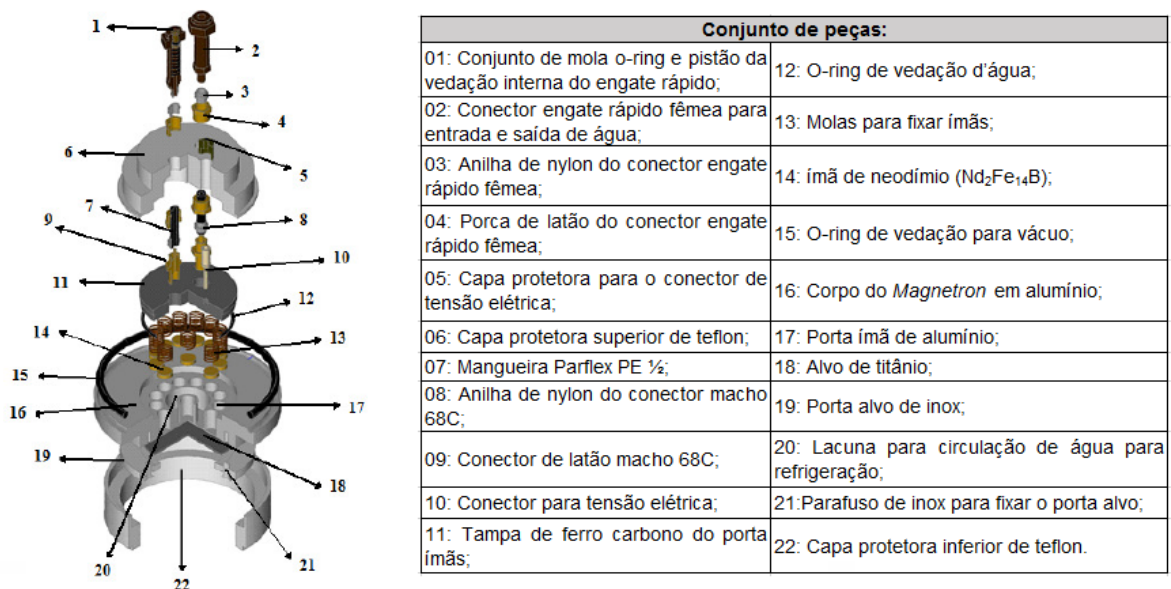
Desenho 3D do Magnetron sputtering. [6]
